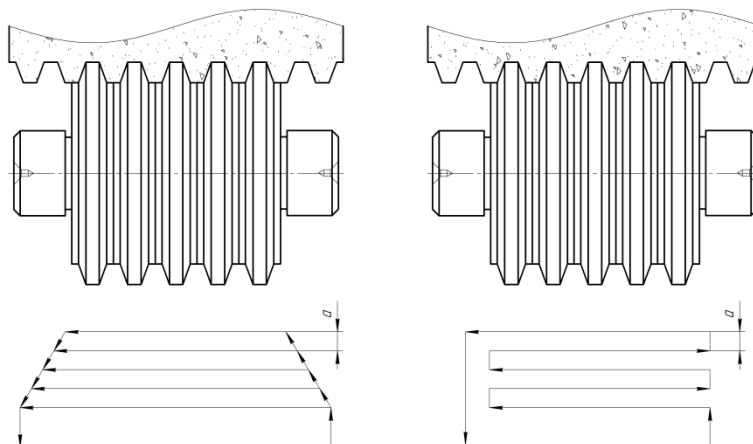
Схемы накатки червячной поверхности гиперboloидного шлифовального круга:
